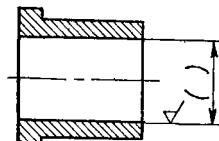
Простановка размеров и шероховатости поверхности детали
